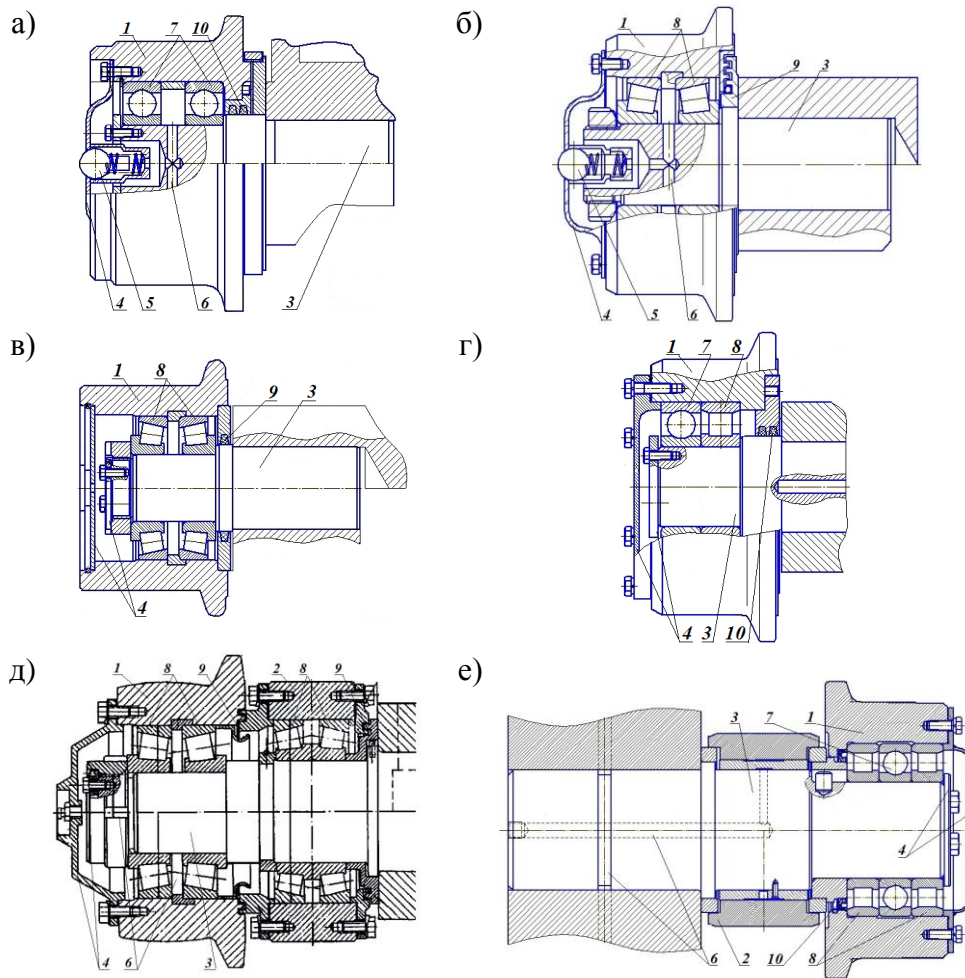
Роликові вузли спікальних та випалювальних візків: 1 – ходовий ролик; 2 – вантажний ролик; 3 – вісь; 4 – кришка; 5 – клапан механізованого змащування підшипників; 6 – канали для змащування підшипників; 7 – кулькопідшипник; 8 – роликпідшипник; 9 – шторне ущільнення; 10 – графенітове ущільнення
